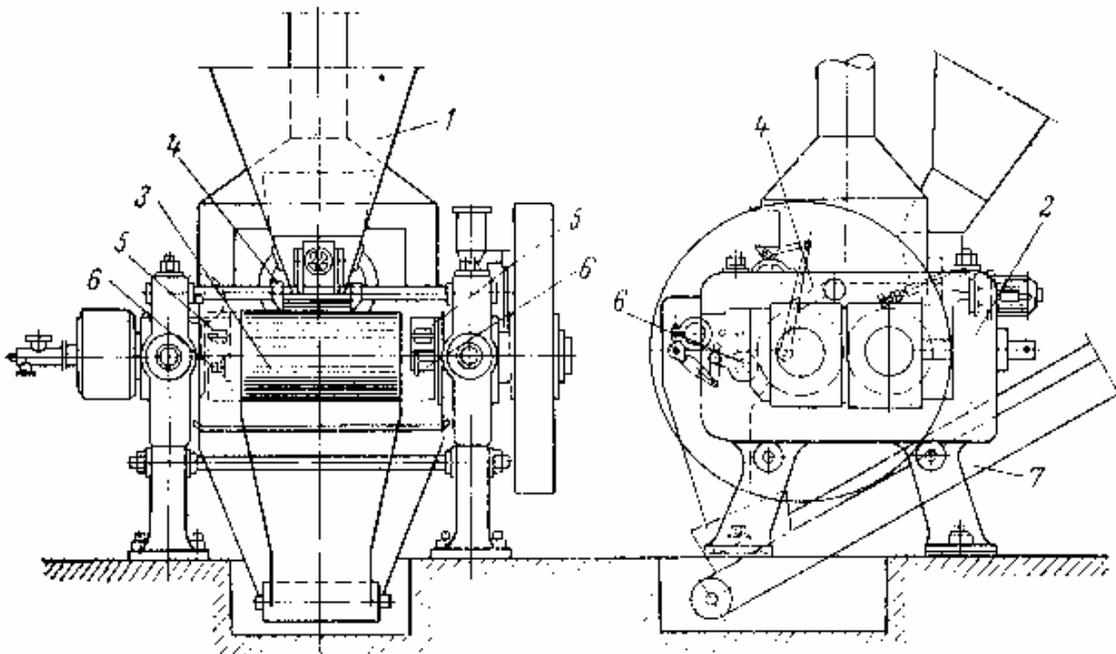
Вальцы для непрерывной пластикации пресс-порошков
